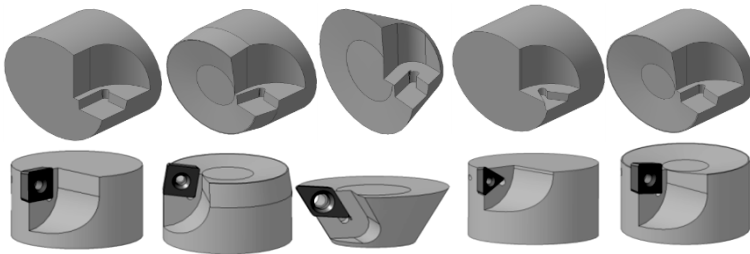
Розміщення БНП на корпусі фрези
